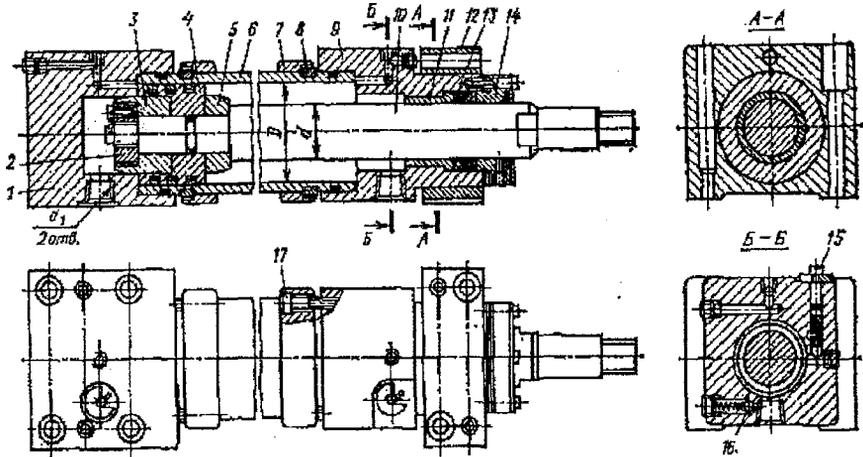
Конструкция гидроцилиндра с односторонним штоком по ОСТ2 Г21-1 – 73 [17]: гильза 6; крышки 1,9; поршень 4; шток 10; разрезная гайка 2; тормозные втулки 3,5; фланец 7; полукольцо 8; втулка 11; передняя опора 12; крышка 14; дроссель 15; обратные клапаны 16; винты 17.
